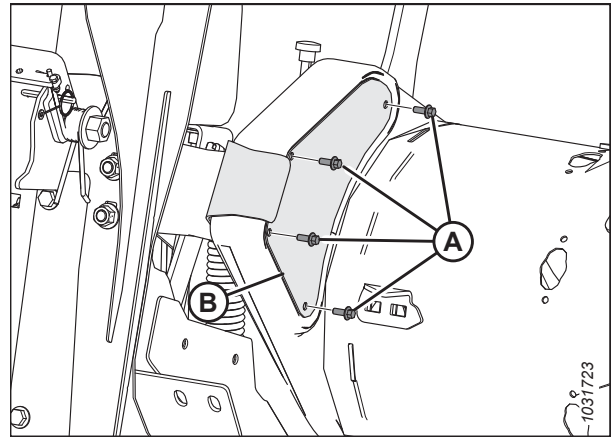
Linke Seite des Einzugsschnecke-Getriebes – Rückansicht
